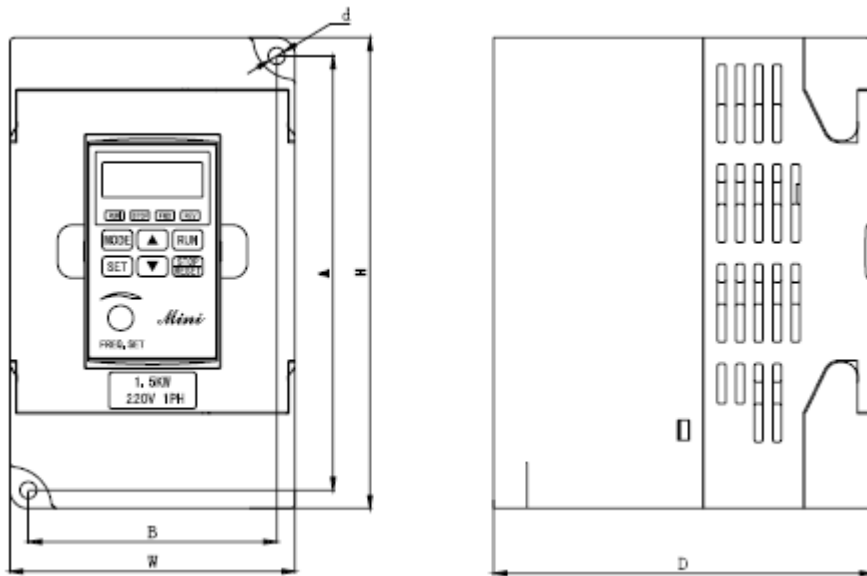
Габаритный чертеж преобразователя частоты
